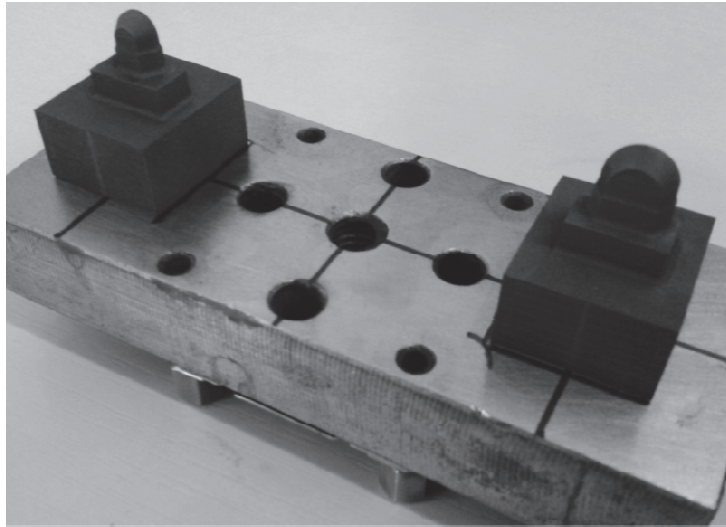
Nástroje pro frézování elektrody pro zácvaky.
